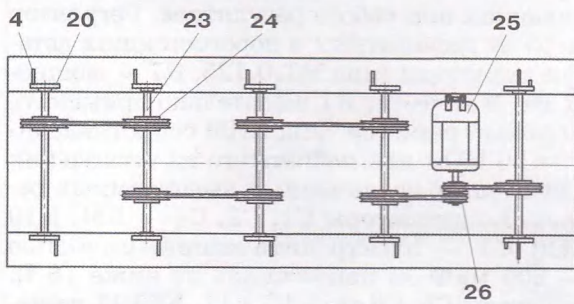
Схема привода валов: 4 — ось кривошипа эксцентрика; 20 — эксцентрик; 23 — вал; 24 — шкив вала; 25 — электродвигатель; 26 — шкив электродвигателя.
